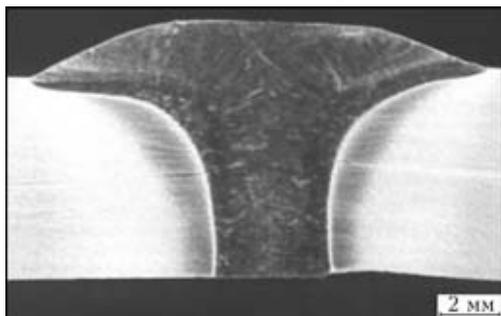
Поперечные сечения сварного шва в стенке трубы (Ду 273x5 мм), полученного гибридной сваркой
